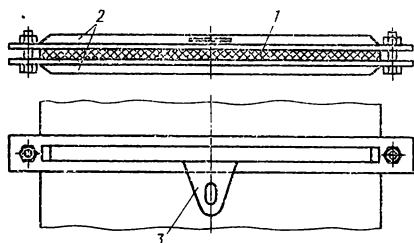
Приспособление для натяжения ремней и транспортной ленты:
